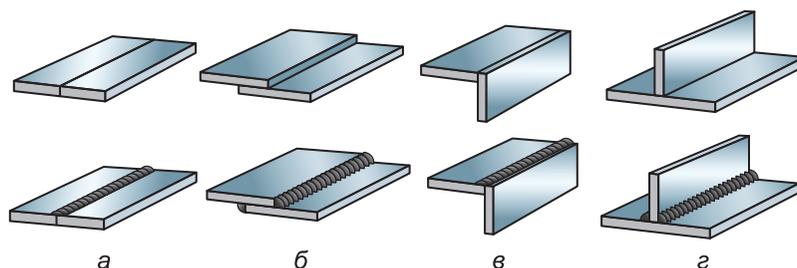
Виды сварочных соединений: а – стыковые; б – накладные; в – угловые; г – тавровые
